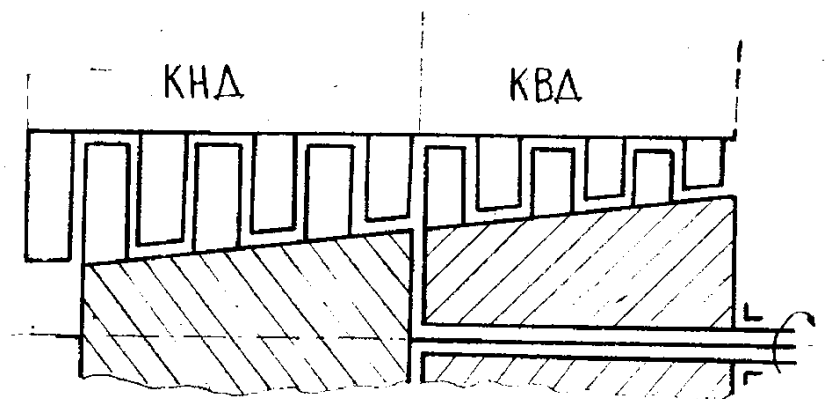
Многоступенчатый осевой компрессор двухвальной схемы
